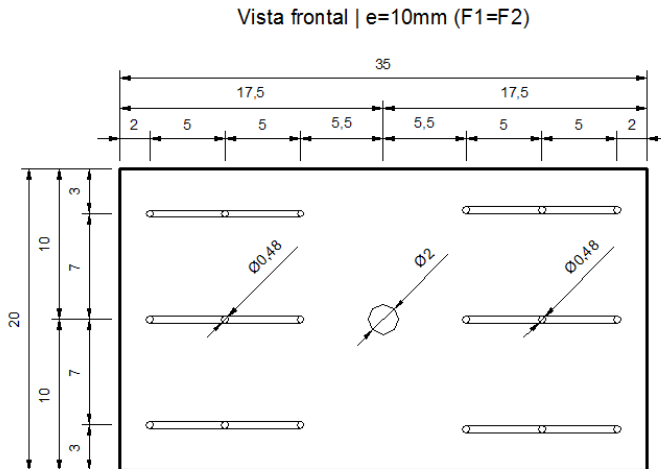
Detalhe das faces F1 e F2, dimensões em cm.
